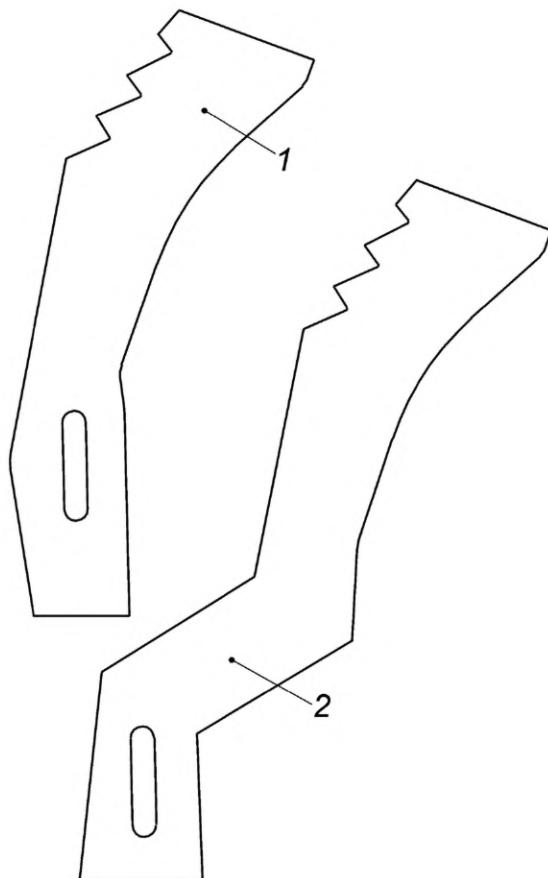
Регулировка расклинивающего ножа и прижима
